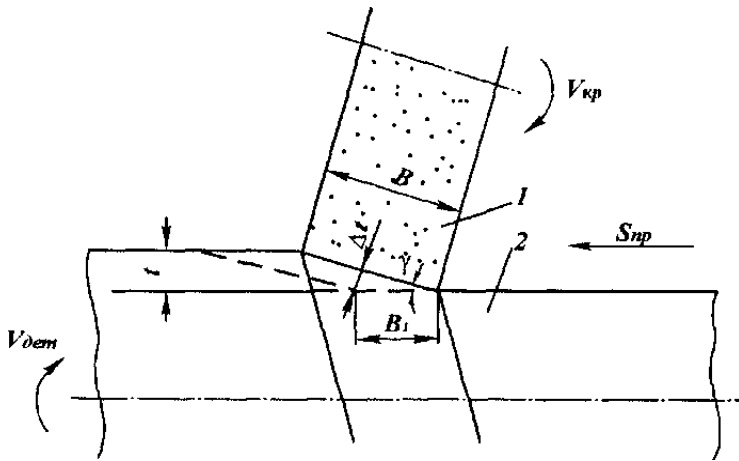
Расчетная схема круглого продольного глубинного шлифования: 1 - круг; 2 - деталь.
